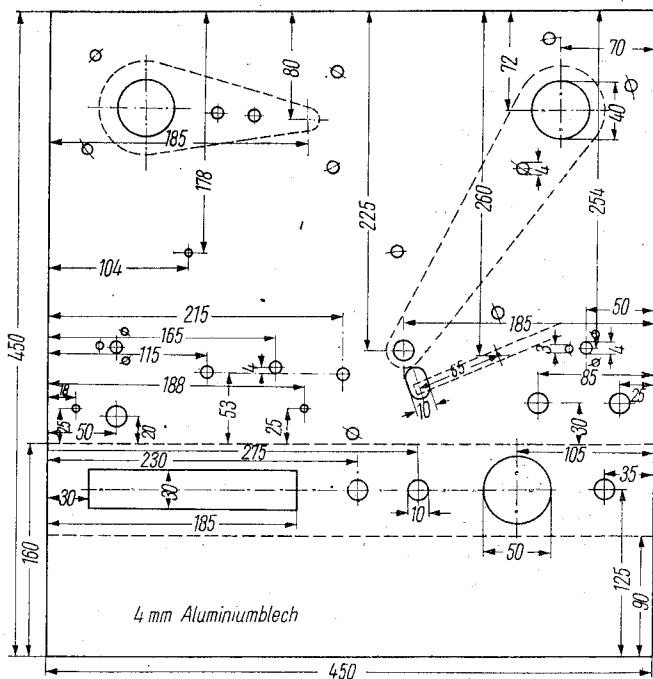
Chassisplatte – Das Chassis wird aus 4 mm Alu gebogen
